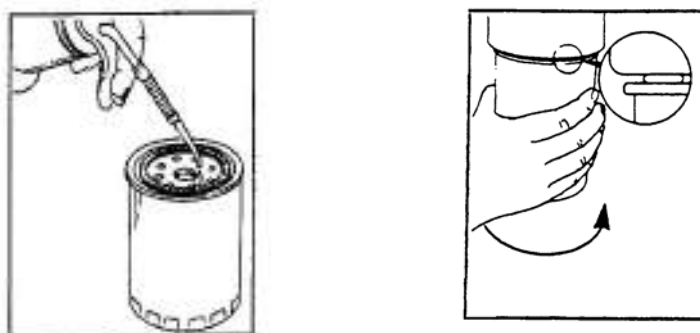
Подготовка и установка фильтра охлаждающей жидкости
